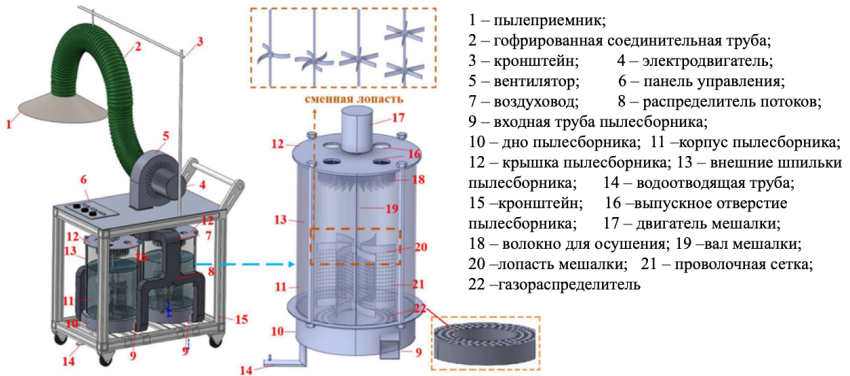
Конструкция новой передвижной водяной пылеулавливающей установки с перемешивающими лопастями
